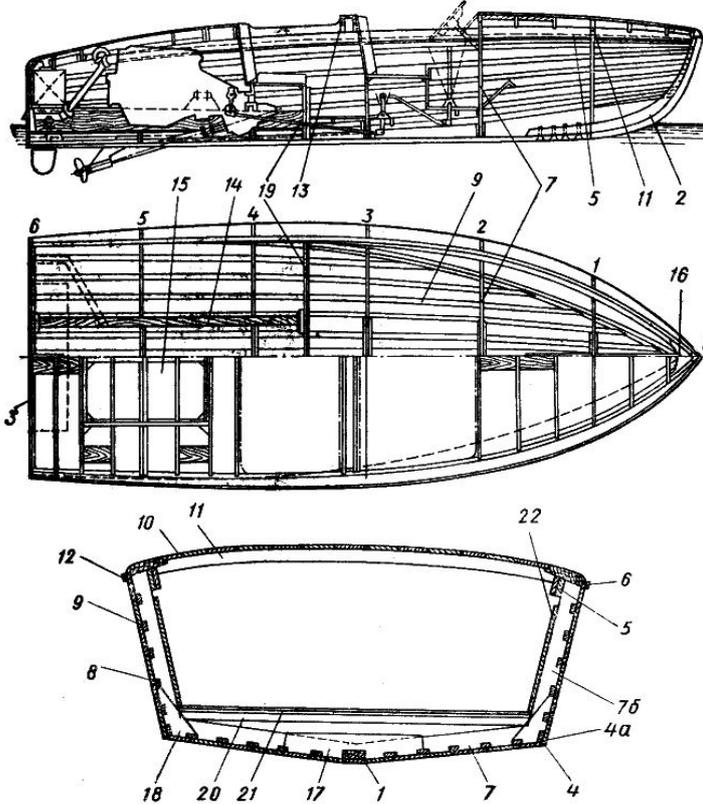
Конструктивный чертеж быстроходного катера: 1 — киль; 2 — форштевень; 3 — транец; 4 — скуловой стрингер; 4a — скуловая планка; 5 — привальный брус; 6 — планширь (ватервейс); 7 — флортимбер; 7a — топтимбер; 8 — наружная обшивка; 9 — пазовая рейка; 10 — настил палубы; 11 — бимс; 12 — буртик; 13 — комингс; 14 — брус фундамента; 15 — надмоторный люк; 16 — брештук; 17 — кница; 18 — скуловая кница; 19 — водонепроницаемая переборка; 20 — лежни слани; 21 — слань; 22 — внутренняя обшивка
